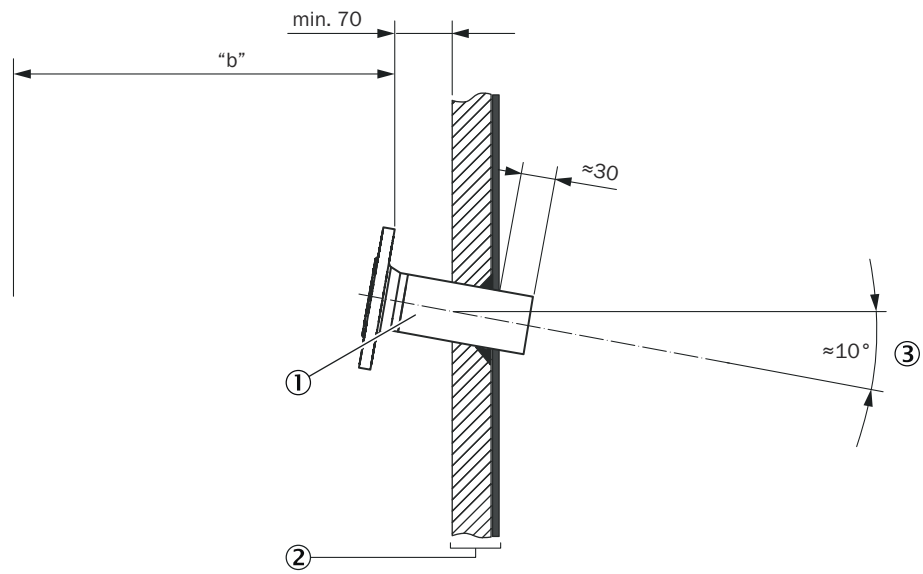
Montagevorgabe Vorschweißflansch
